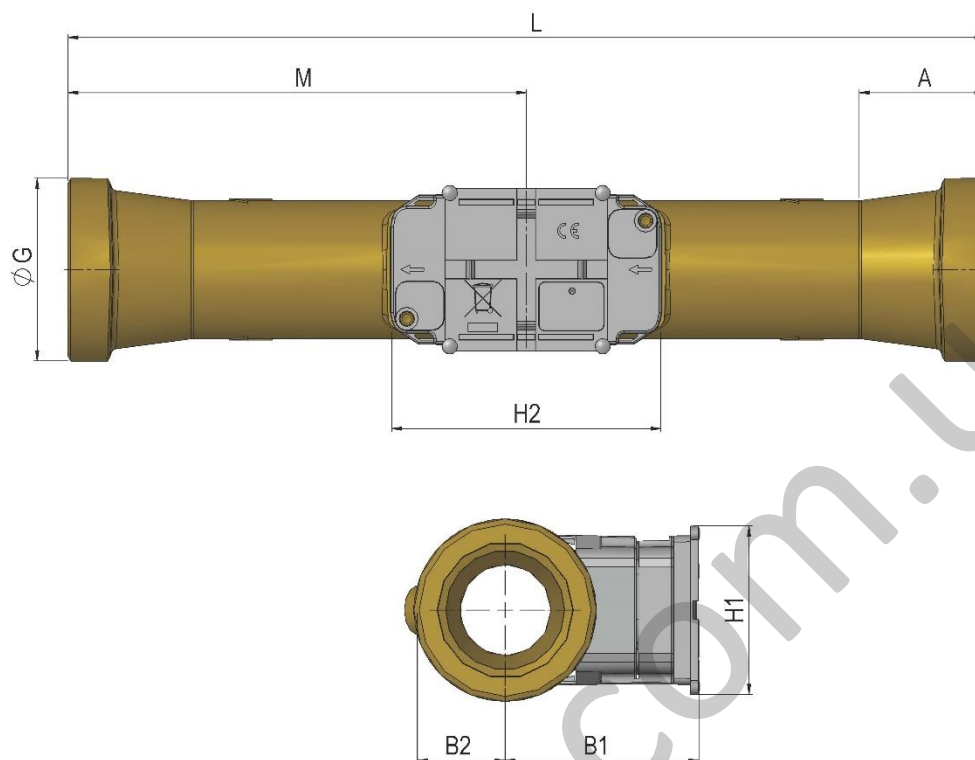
Размерные чертежи ULTRAFLOW® 54 с резьбовым соединением типа 65-5-XXJX-XXX.
